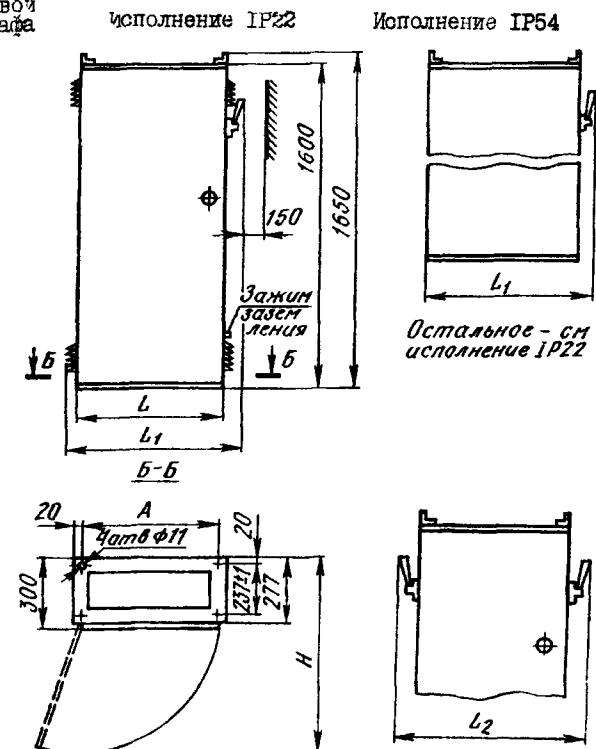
Габаритные, установочные размеры шкафов ШРП
